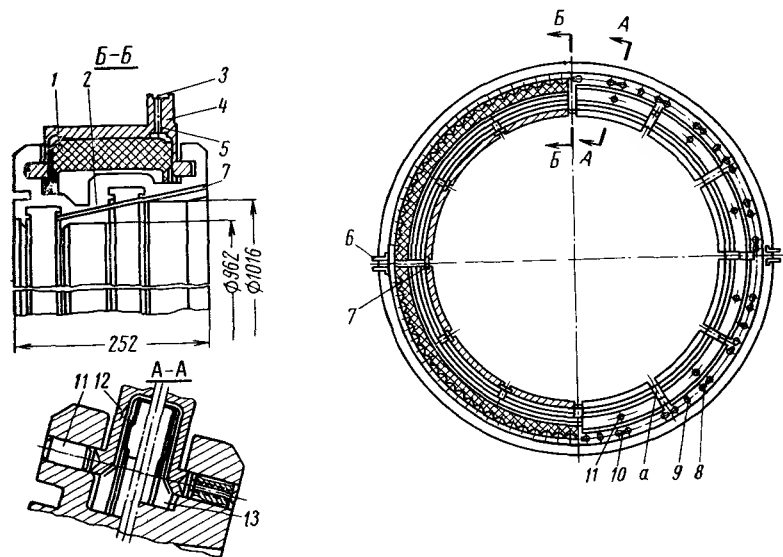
Обойма турбины высокого давления установки ГТ-700-5 НЗЛ
